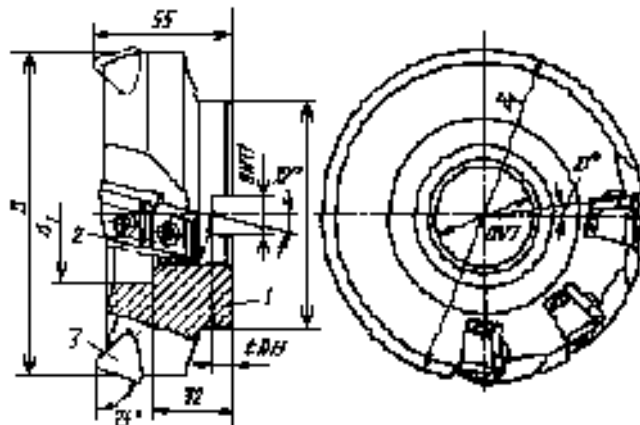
Фреза торц. с 3-гран.пласт.с задн.кутами
